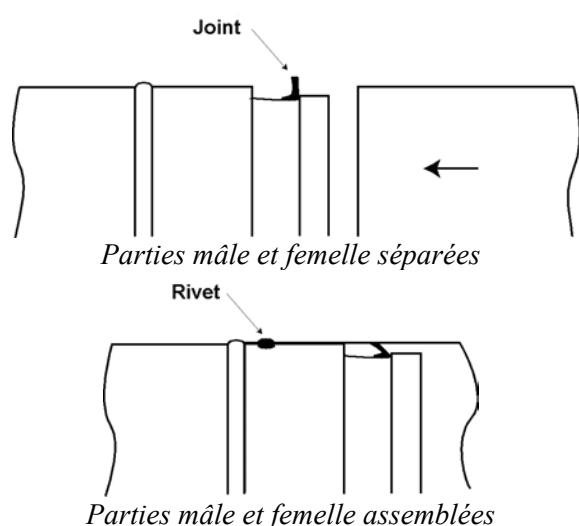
Accessoire à joint pour conduits circulaires (photo : Lindab)
